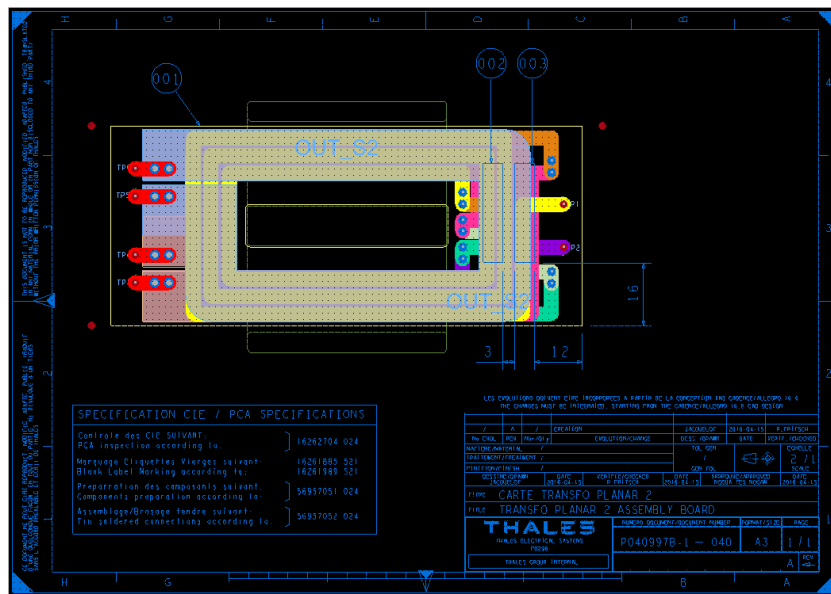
CAO du PCB MC20_N17B (ou Pc_Sc)
